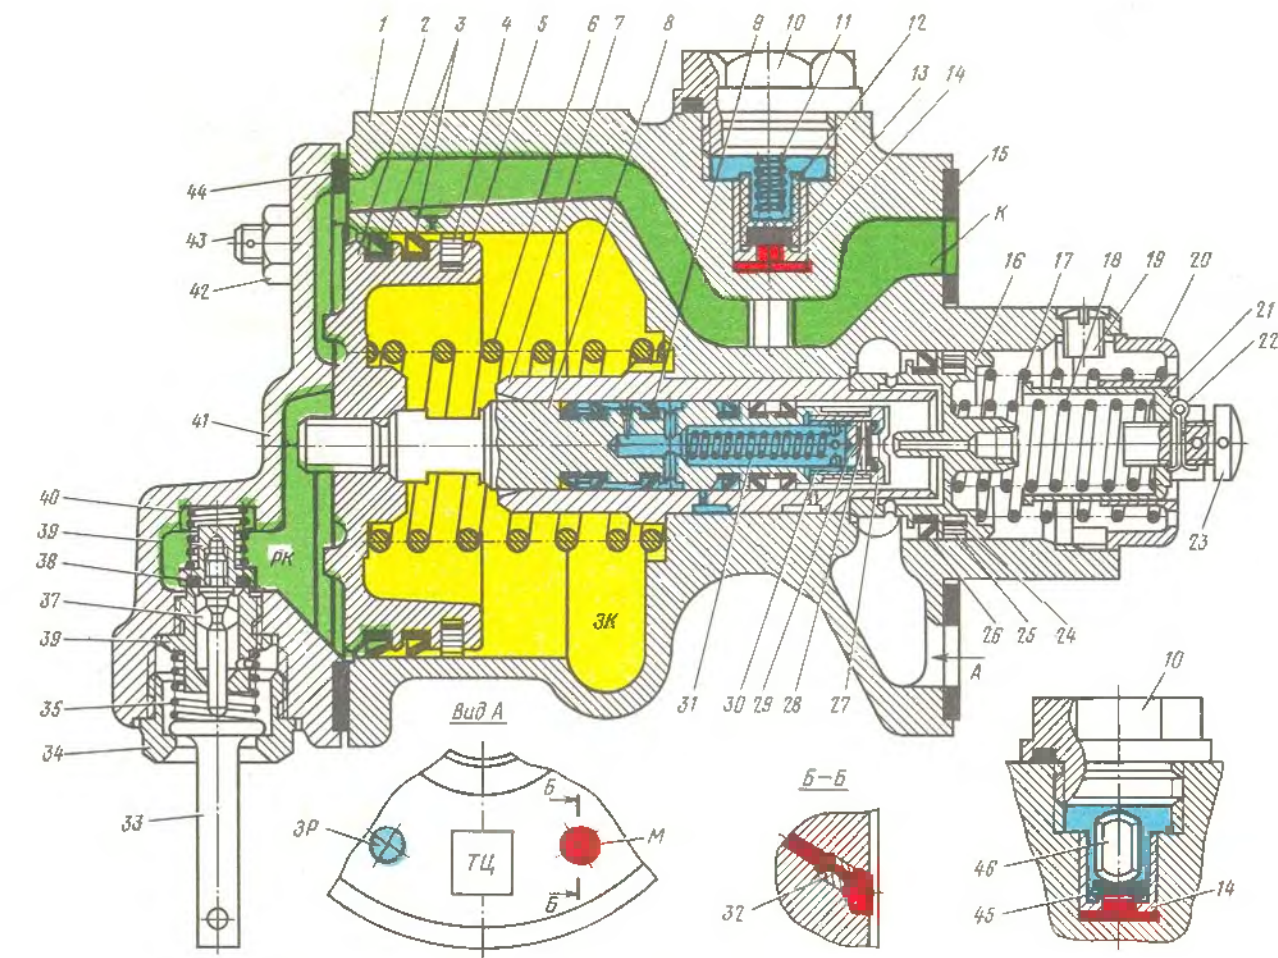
Главная часть № 270-023 воздухооросредителя № 270-002, 270-005-1 и 483-000
